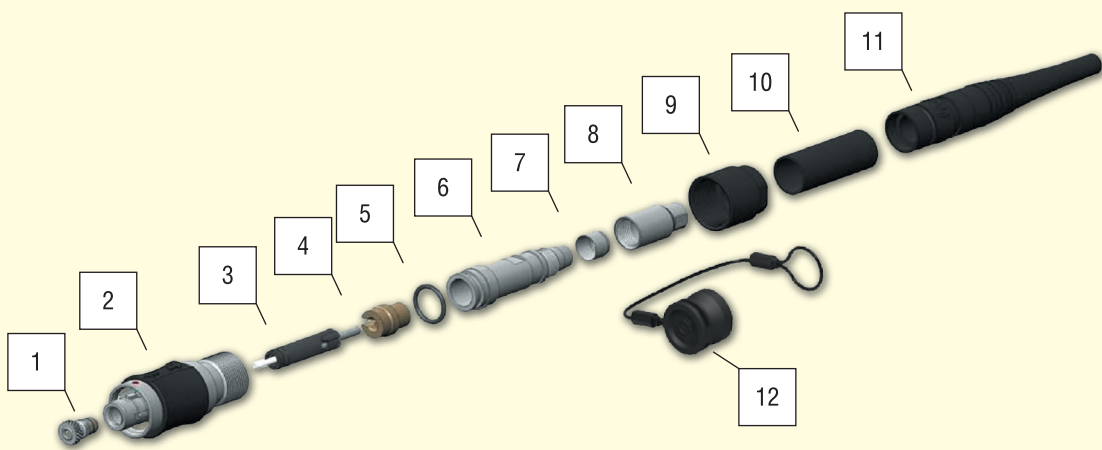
Складові частини з'єднувача (з прикладу FO1): 1 — наконечник; 2 — корпус з'єднувача; 3 — оптоволоконний контакт (ферула); 4 — тримач контакту; 5 — кільце ущільнювача типу O-ring; 6 — гільза (корпус затискного механізму); 7 — конічне кільце; 8 — затискна гайка; 9 — задня (стяжна) гайка; 10 — термозбіжна трубка; 11 — хвостовик; 12 — захисний ковпачок (заглушка)
